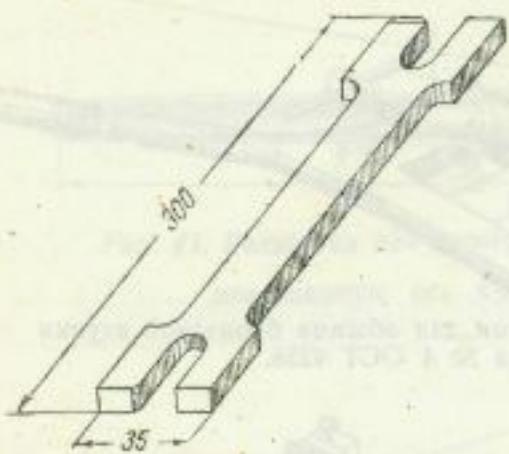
Приспособление для правки стоеч вертлюга и тяг ПМ-25.
